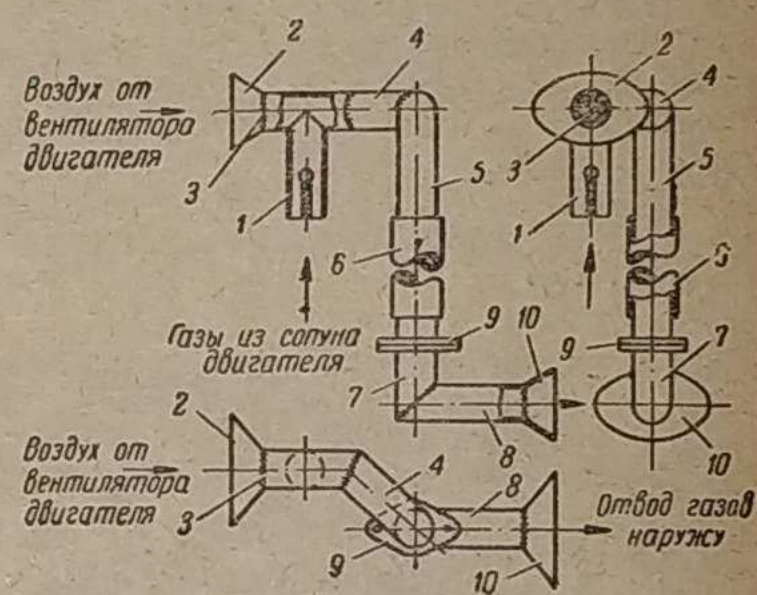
Устройство для отсасывания газов из картера двигателя: 1 — патрубок газопоглотителя, 2 — уловитель, 3 — сетчатый съемный фильтр, 4, 5, 7, 8 — газоотводные патрубки, 6 — гибкий шланг, 9 — фланец, 10 — эллипсоидный щиток.
